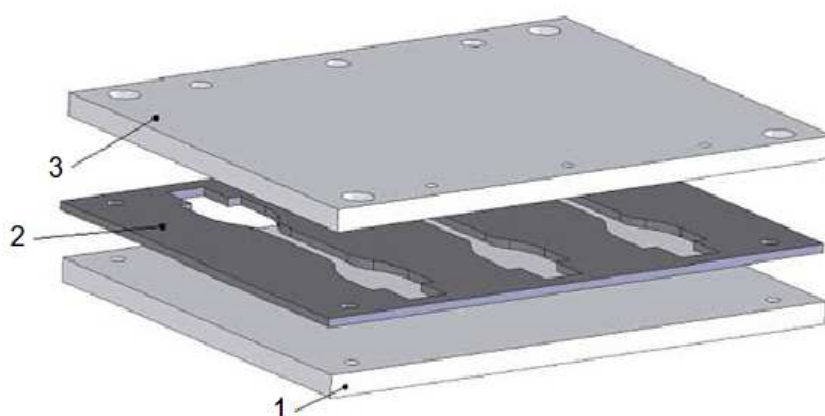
Vista explodida do molde utilizado no método de fabrico de provetes de adesivo por moldação: 1 – Placa inferior, 2 – Placa intermédia, 3 – Placa superior [32 e 33].
